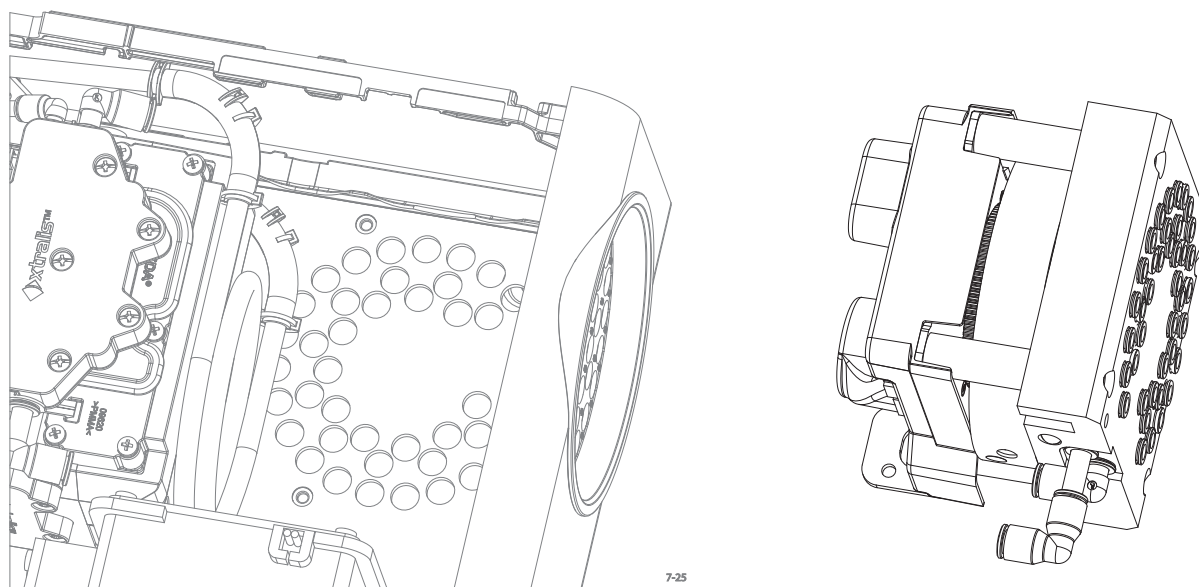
Извещатель после демонтажа поворотного клапана
